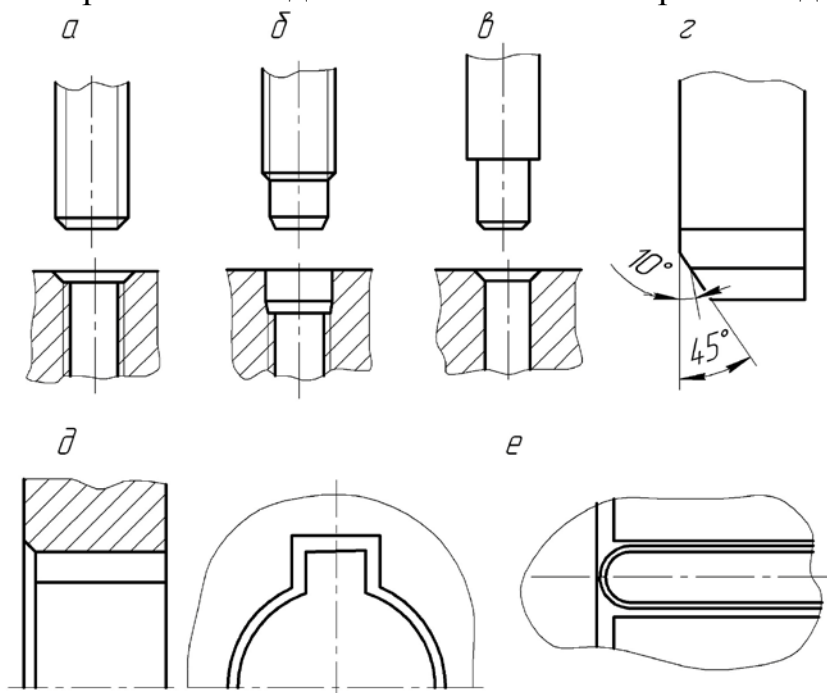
Технологичные конструкции заходных поверхностей соединяемых деталей в соединениях: а, б – резьбовых; в, г – гладких цилиндрических; д, е – шпоночных
